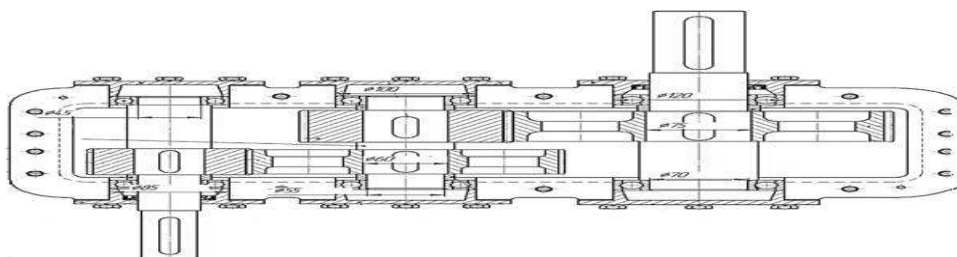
Чертеж двухступенчатого цилиндрического редуктора
